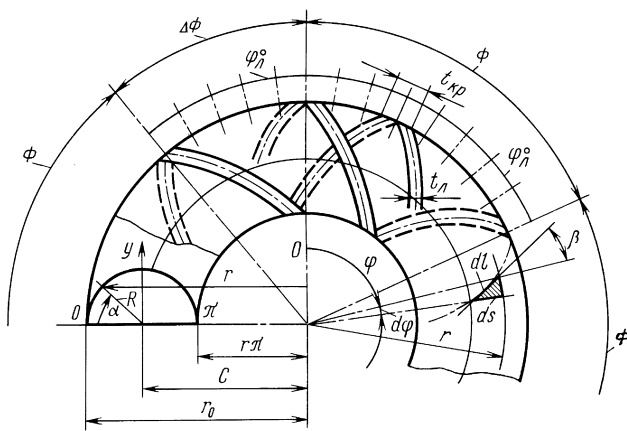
Параметры намотки и схема укладки витков ленты из нитей на поверхности торовой оболочки
